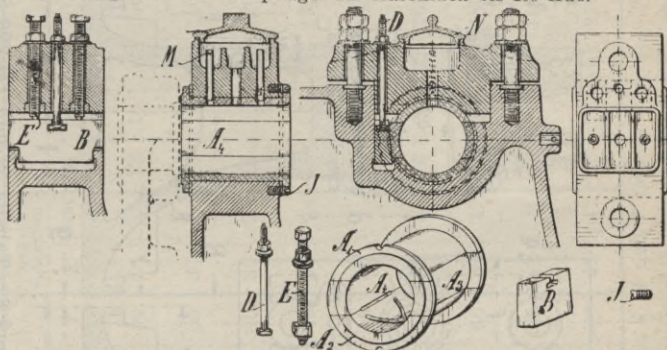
262. Hauptlager für Maschinen bis 900 Hub (Seite 94).
